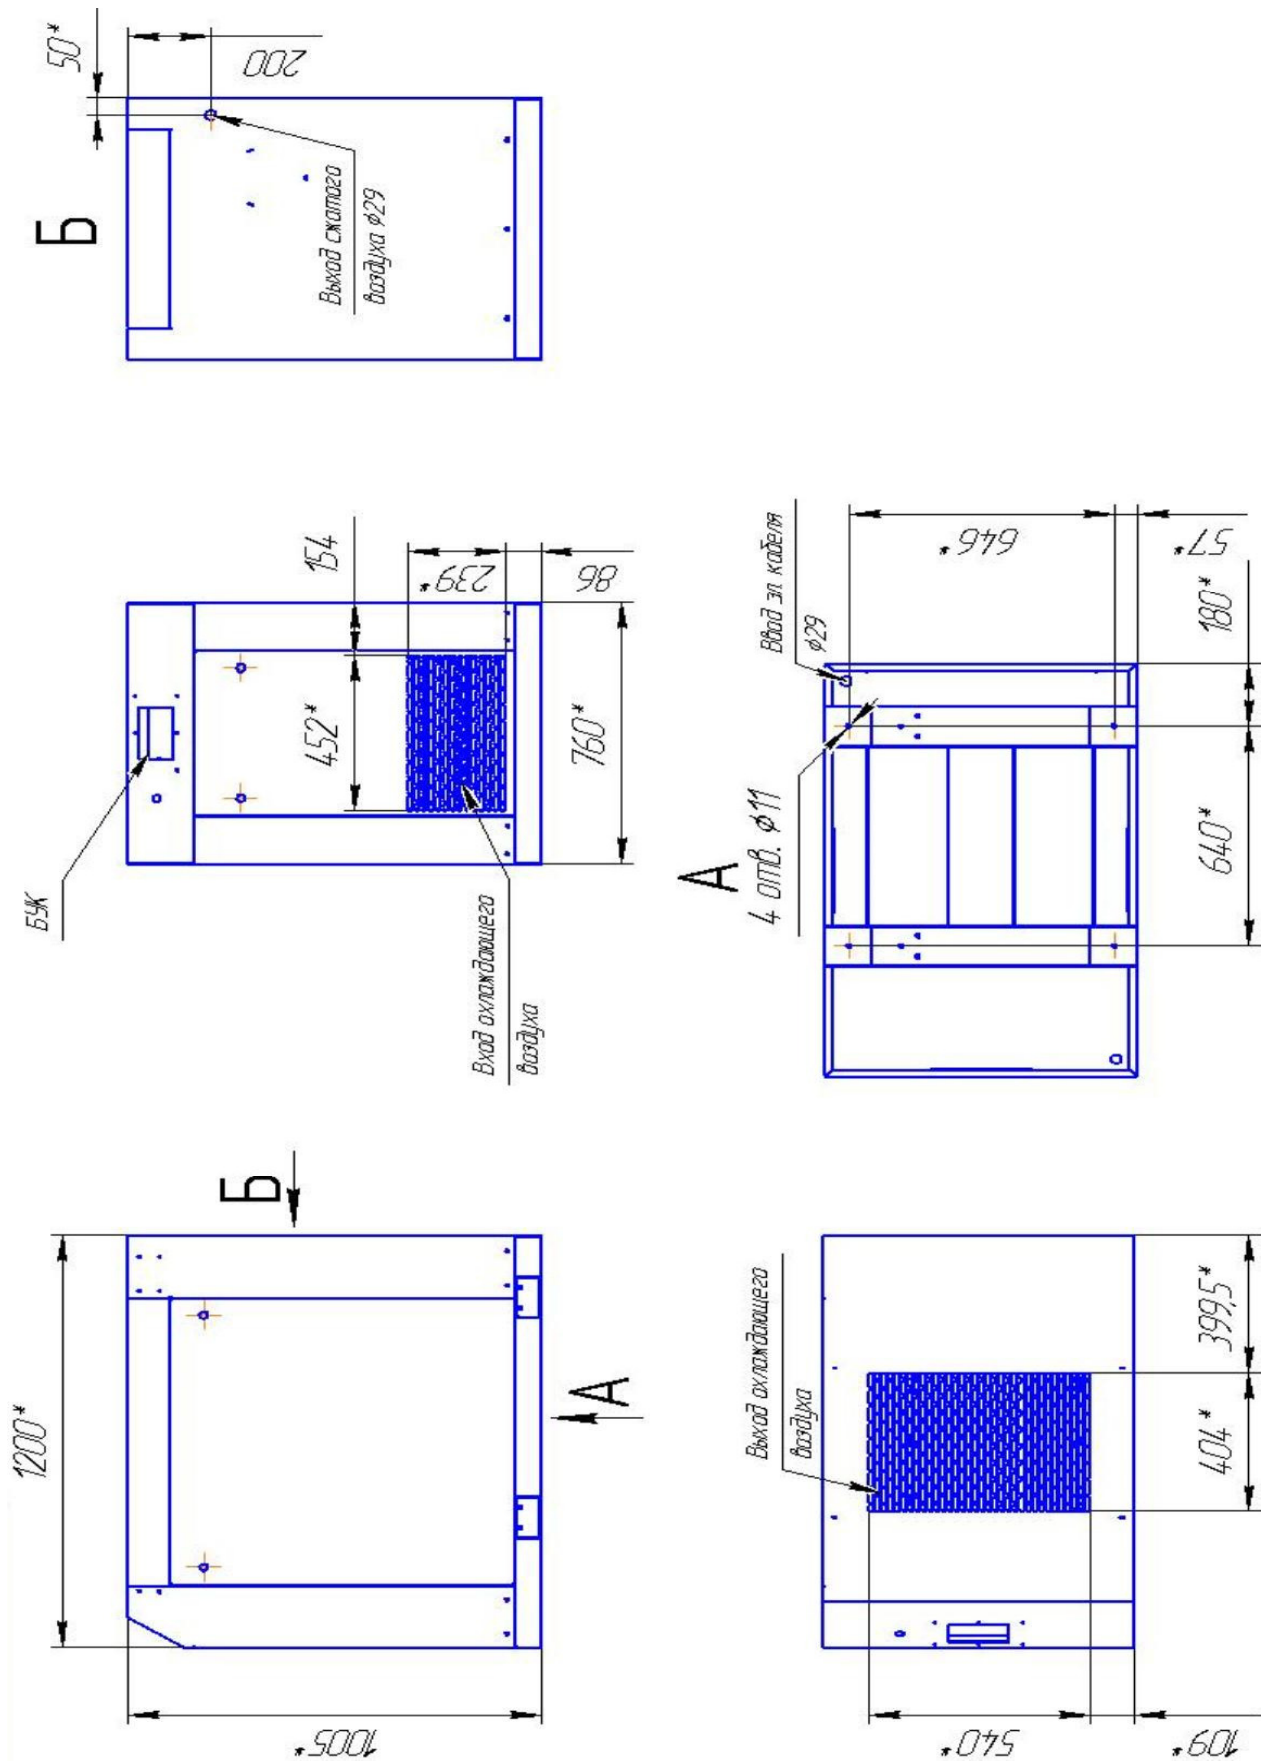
Габаритный чертеж установок ДЭН-15Ш, ДЭН-18Ш, ДЭН-22Ш и ДЭН-30Ш (6022)
